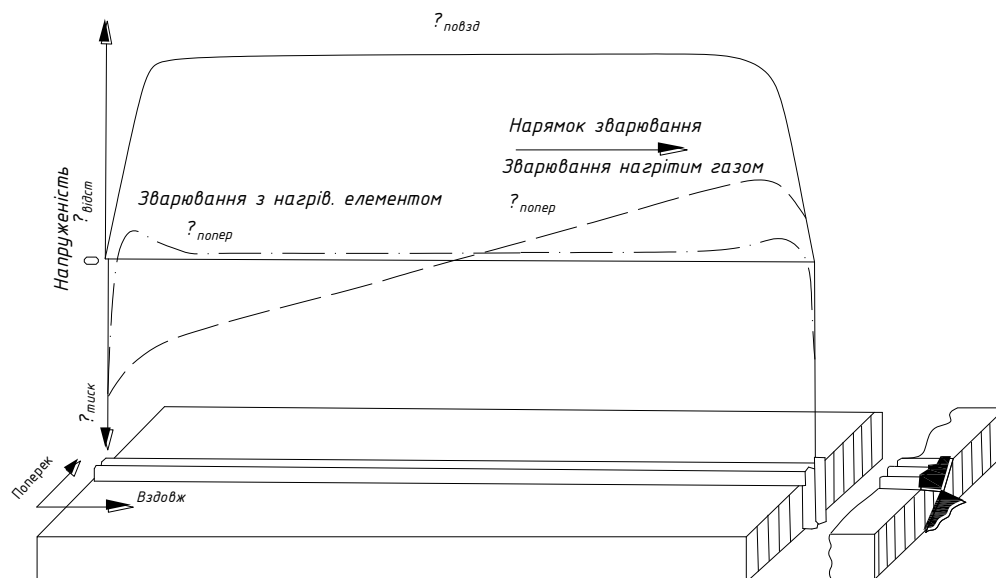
Графік зміни напруг зварювання по довжині зварного шва
